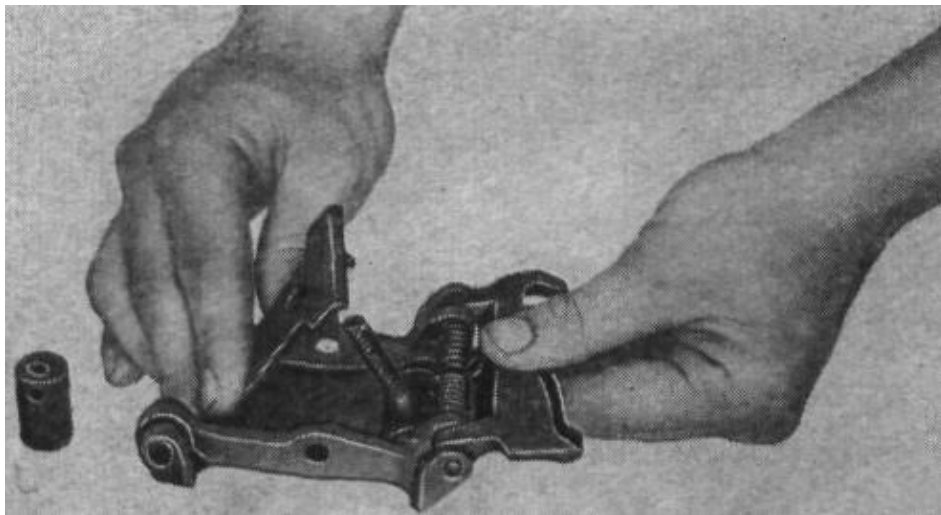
Постановка приспособления для разборки и сборки подающих пальцев
